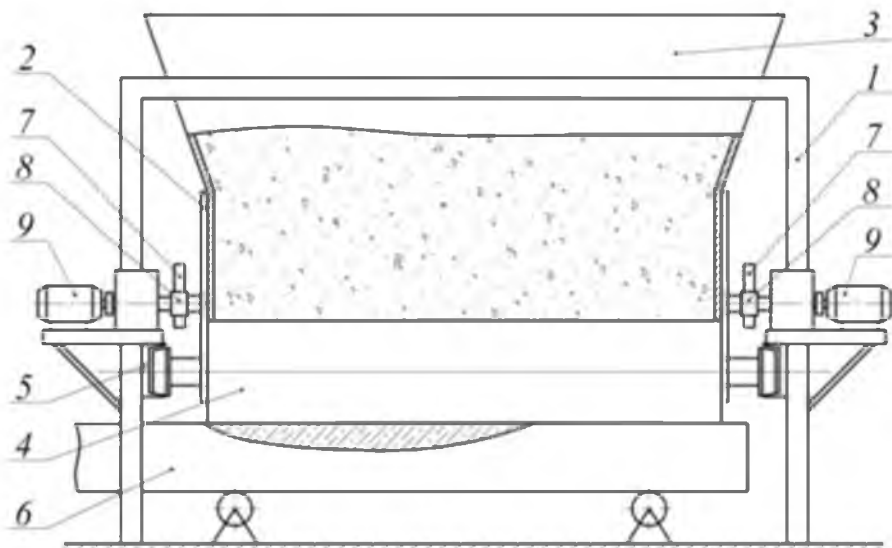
Роликова формувальна установка з двома кулачковими приводними механізмами
